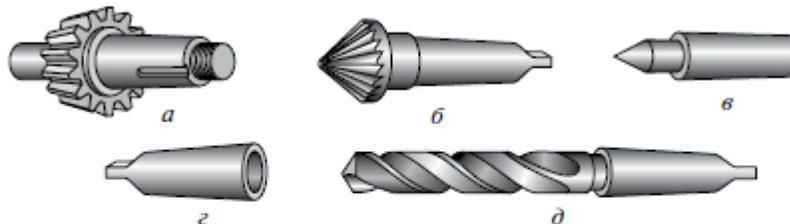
Типовые детали с коническими поверхностями: *а* — коническое зубчатое колесо; *б* — коническая зенковка; *в* — центр токарного станка; *г* — переходная втулка; *д* — сверло с коническим хвостовиком
